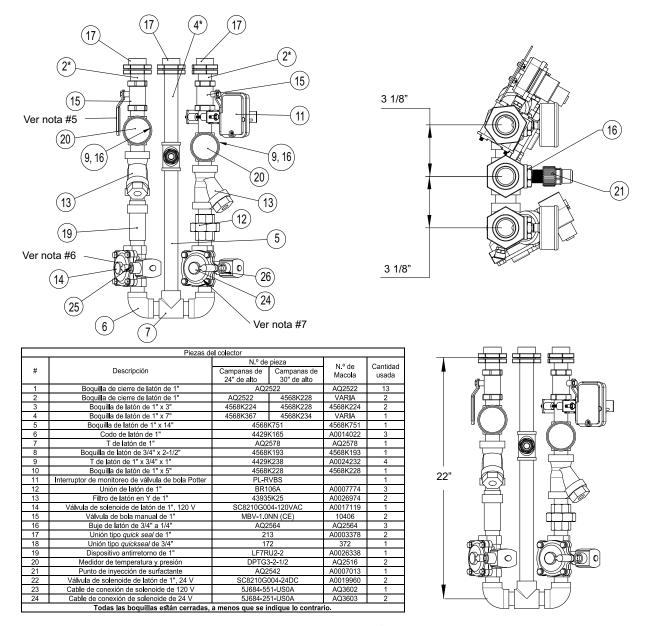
Detalle de autolimpieza de 3/4" con colector de gabinete utilitario de montaje en pared CORE
